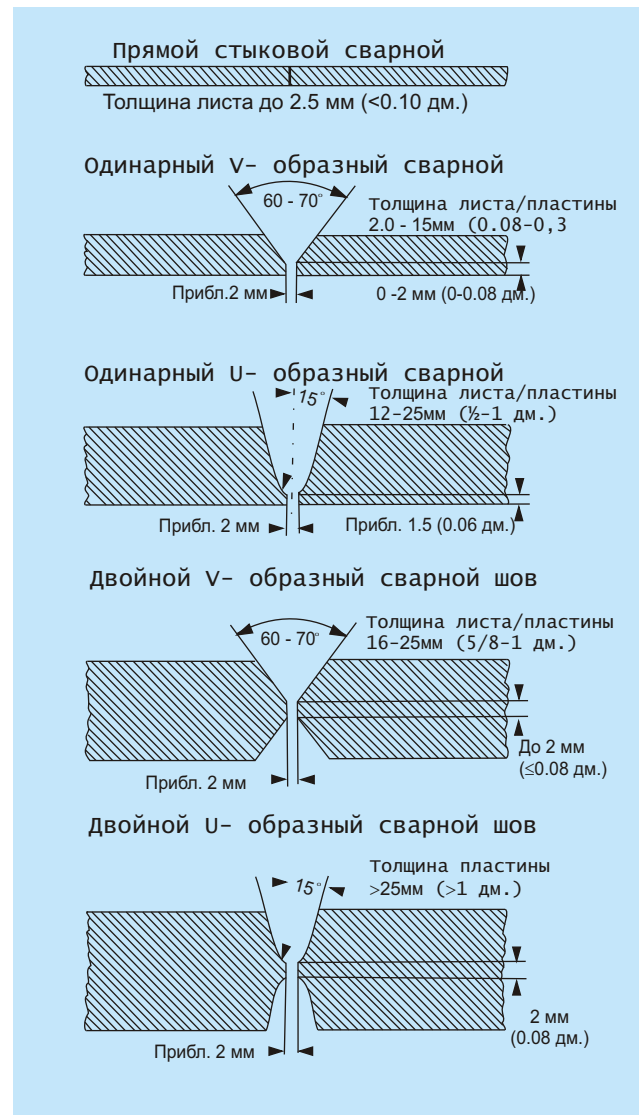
Подготовка кромок для сваривания никелевых сплавов и специальной нержавеющей стали
